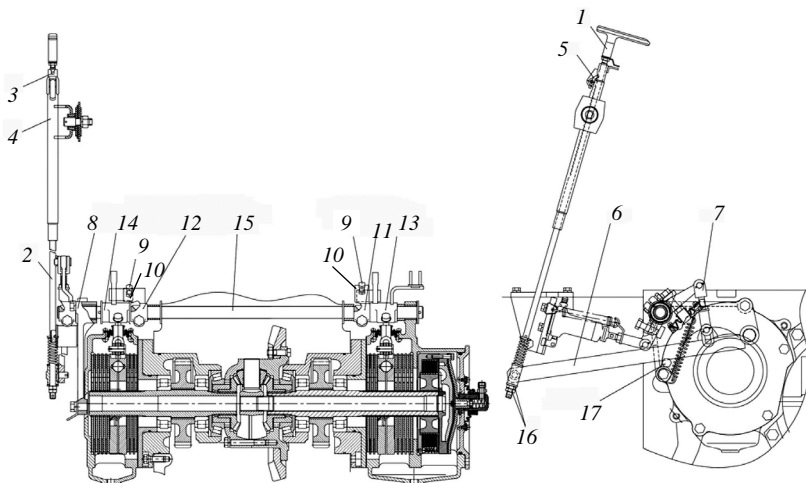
Регулировка привода стояночного тормоза: *1* – рукоятка; *2, 7* – тяги; *3* – штифт; *4, 8* – кронштейны; *5* – фиксатор; *6* – рычаг; *9* – контргайка; *10* – болт регулировочный; *11, 13* – рычаги правого тормоза; *12, 14* – рычаги левого тормоза; *15* – валик; *16* – гайки; *17* – болт-оправка
